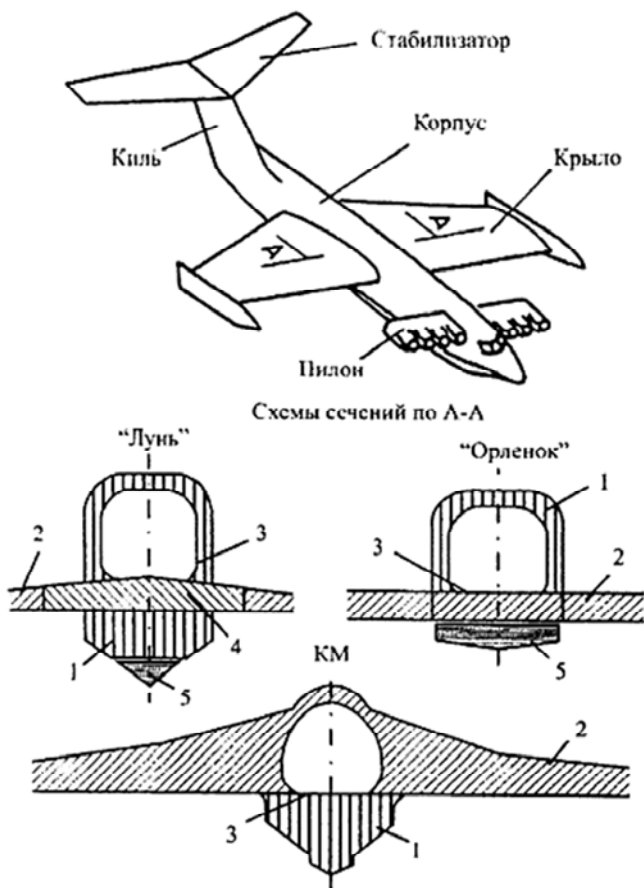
Конструкция планера и схемы соединений корпуса с крылом ЭП:
